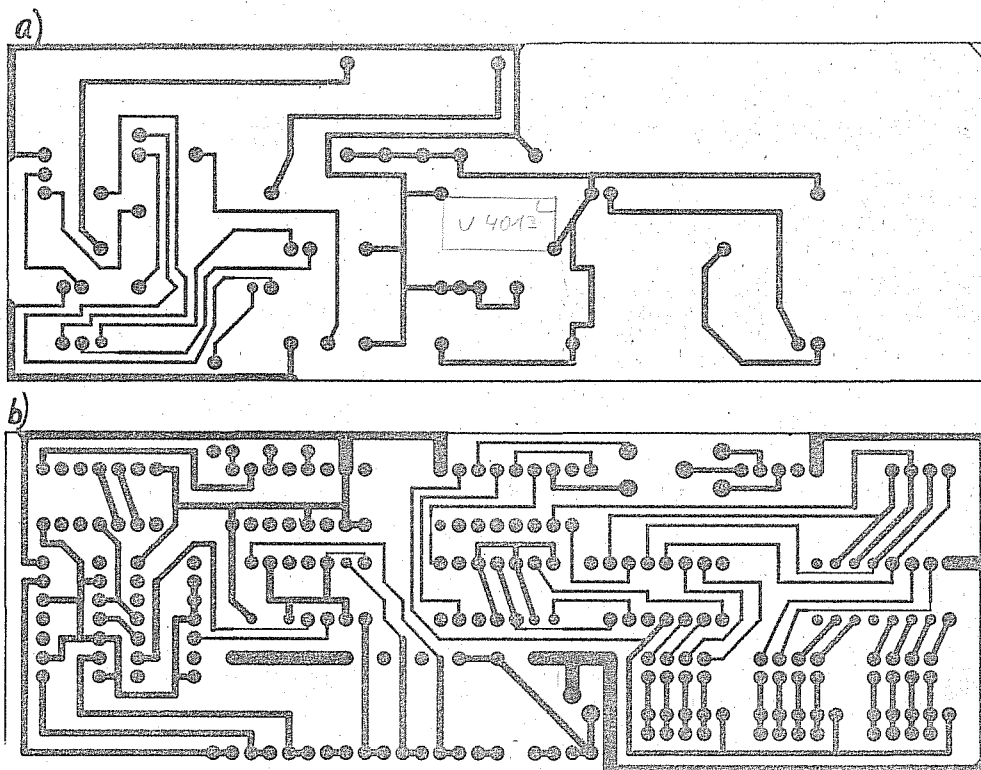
Layout, B-Seite Bild 3b Layout, L-Seite
